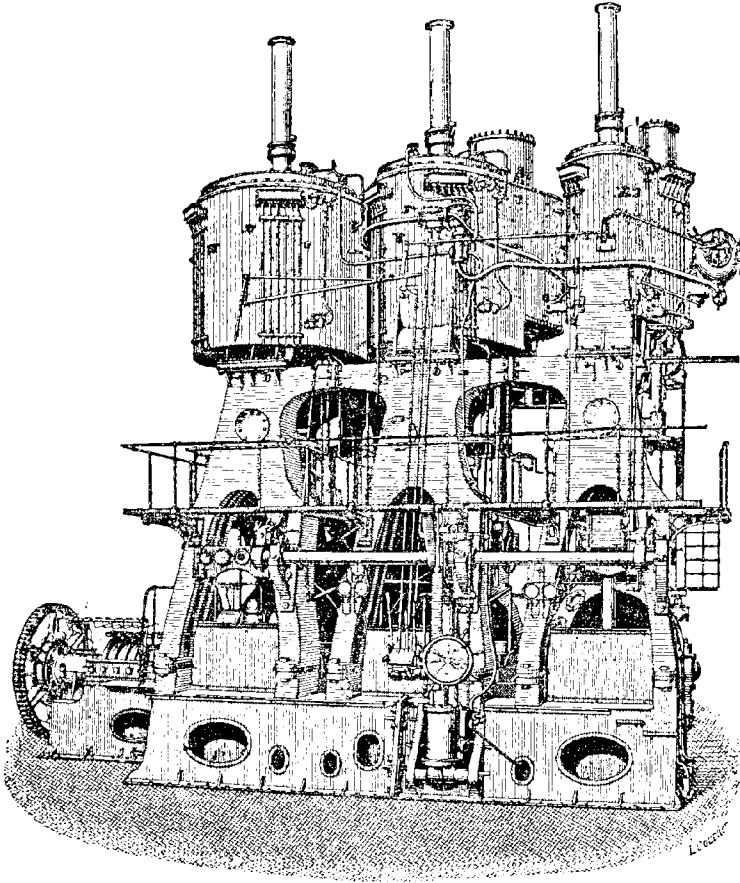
Machine à triple expansion du *Glyde* (vue perspective).
